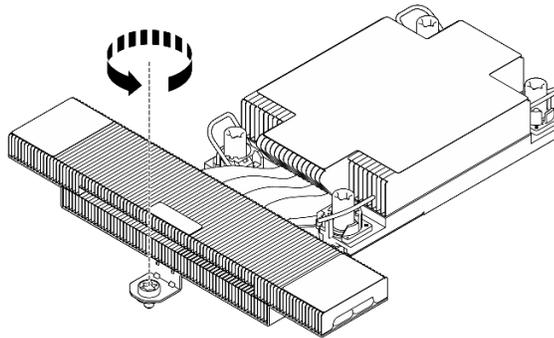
Desserrage des vis du dissipateur thermique en forme de T
